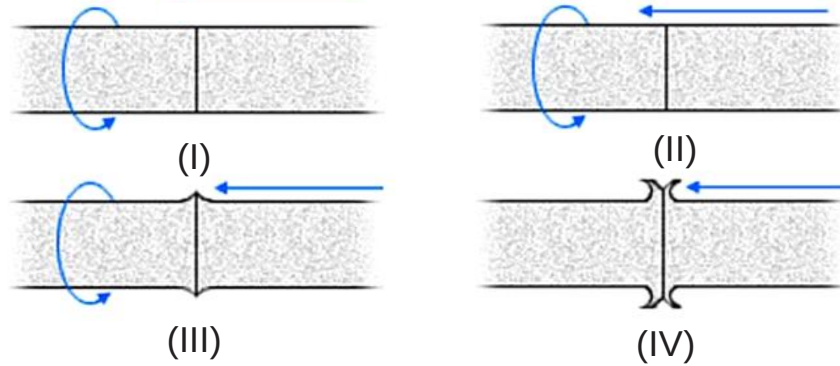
Esquema del proceso de una soldadura por la técnica de RFW.
